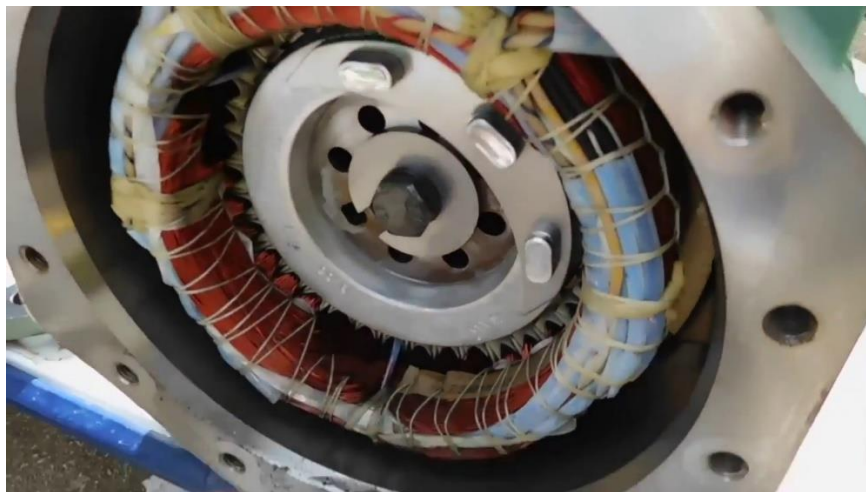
Fig. A : Vue de côté de moteur électrique du compresseur Bitzer.
